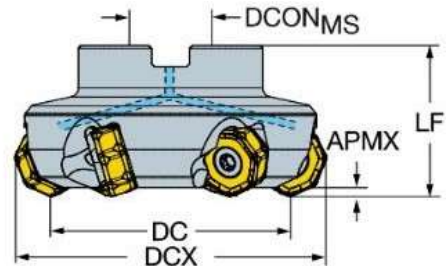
Ескіз торцевої фрези CoroMill 745 Ø80 мм.
